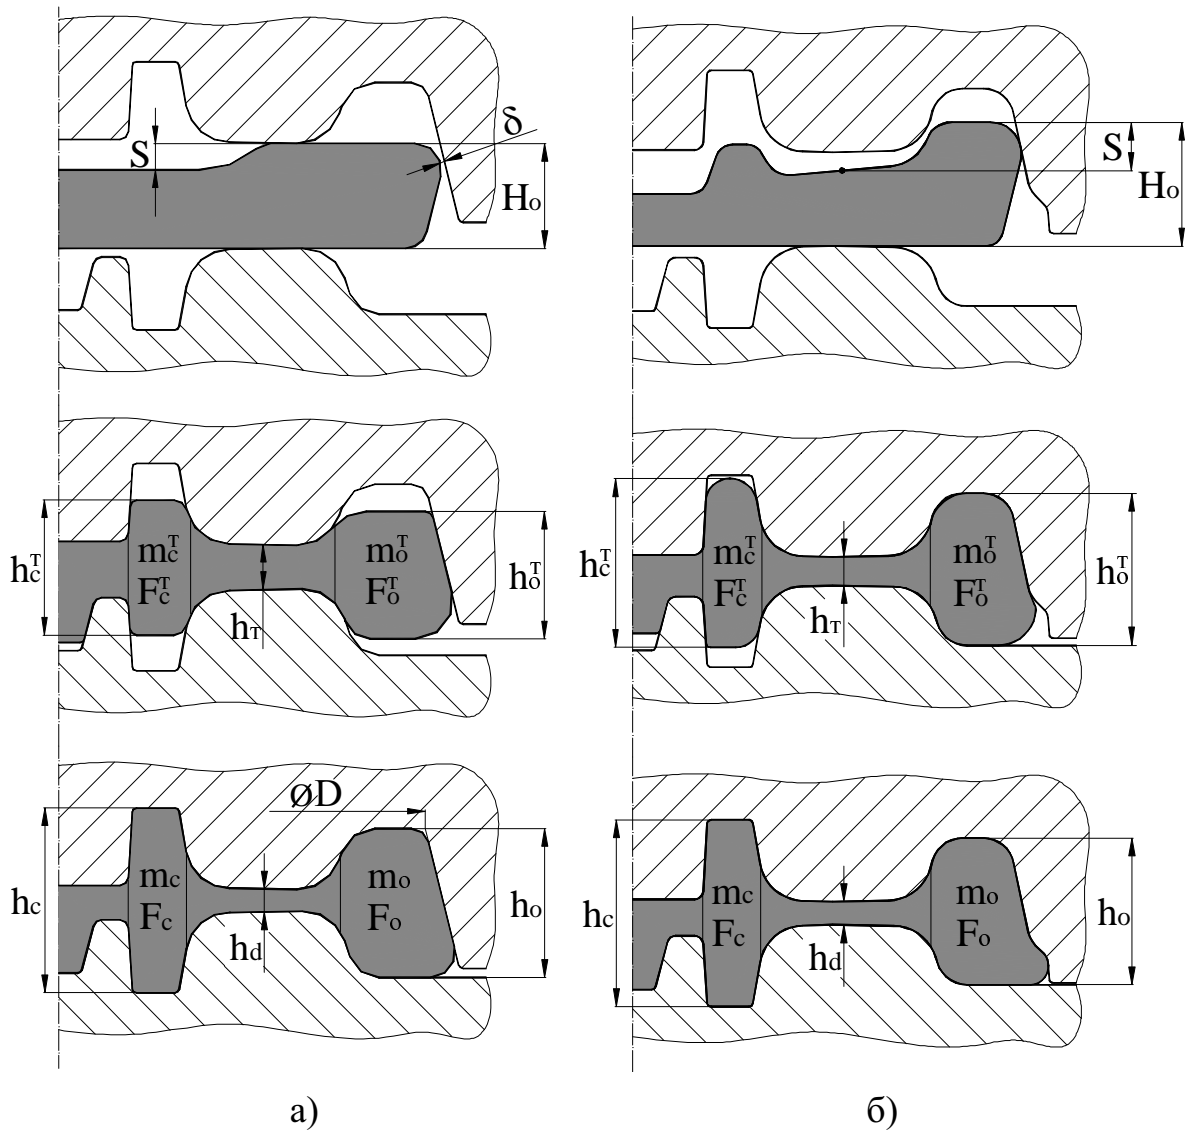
Формовочные штампы и деформируемая в них заготовка:
